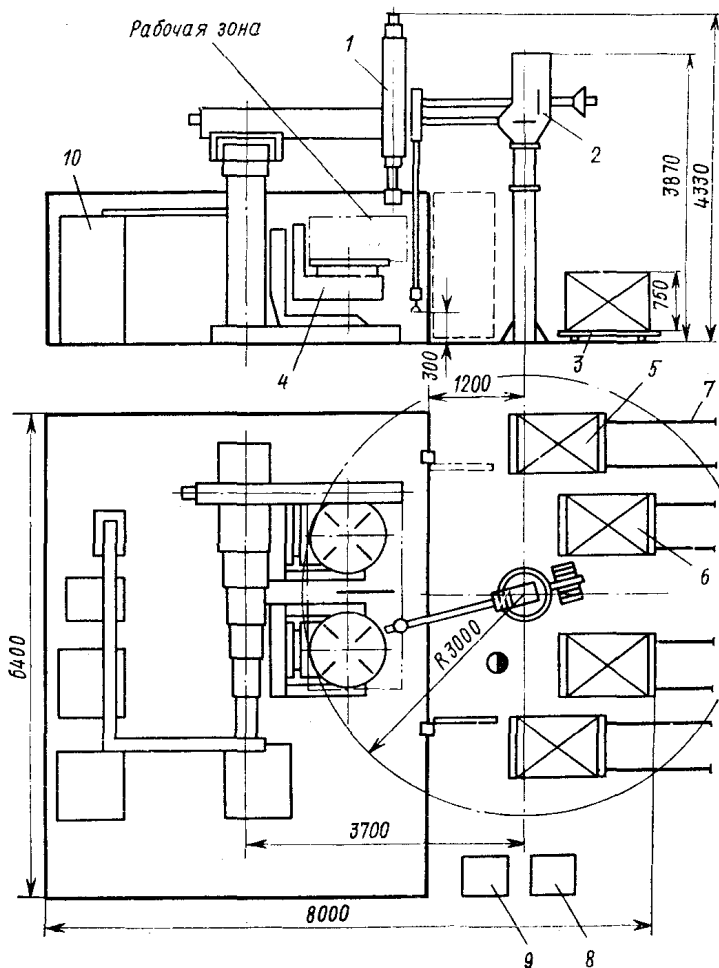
Пример планировки робототехнического комплекса дуговой сварки
